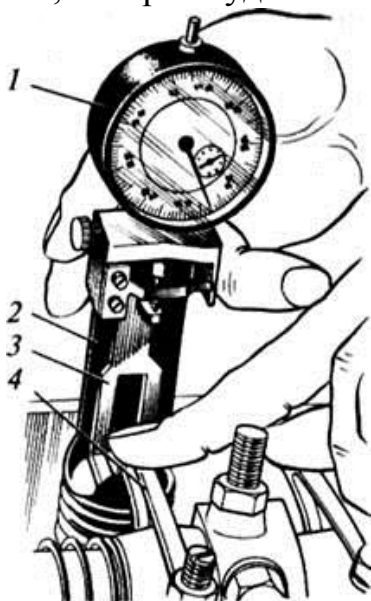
Измерение зазора приспособлением КИ-9918:
